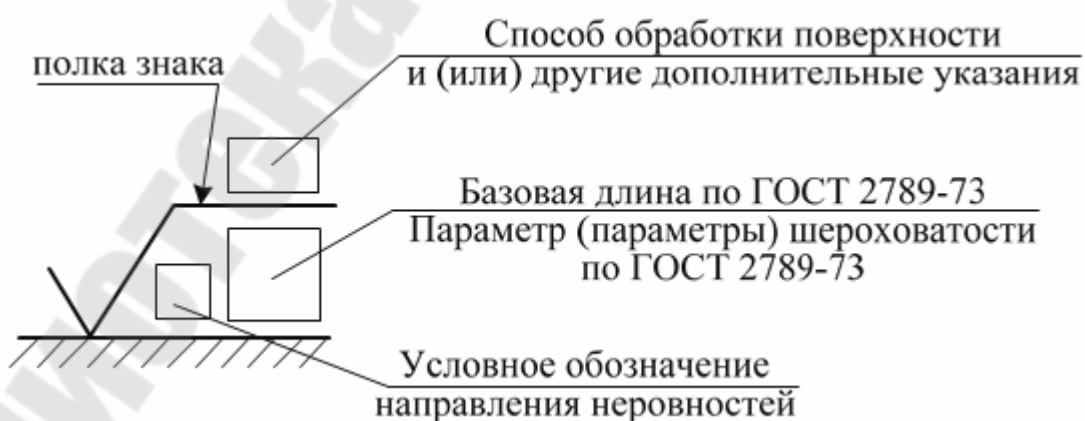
Структура обозначения шероховатости поверхности на чертежах
